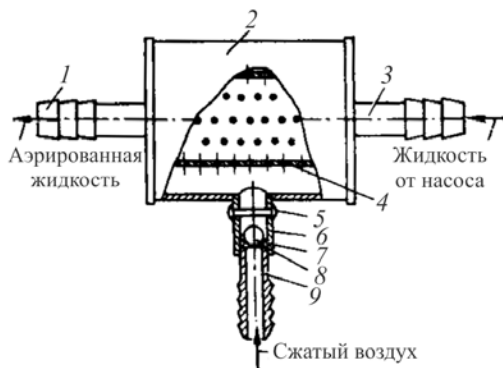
Устройство для ввода сжатого воздуха от компрессора в нагнетательную линию: 1, 3, 6, 9 – патрубки; 2 – корпус; 4 – барботажная трубка; 5 – ограничитель; 7 – шарик; 8 – седло
